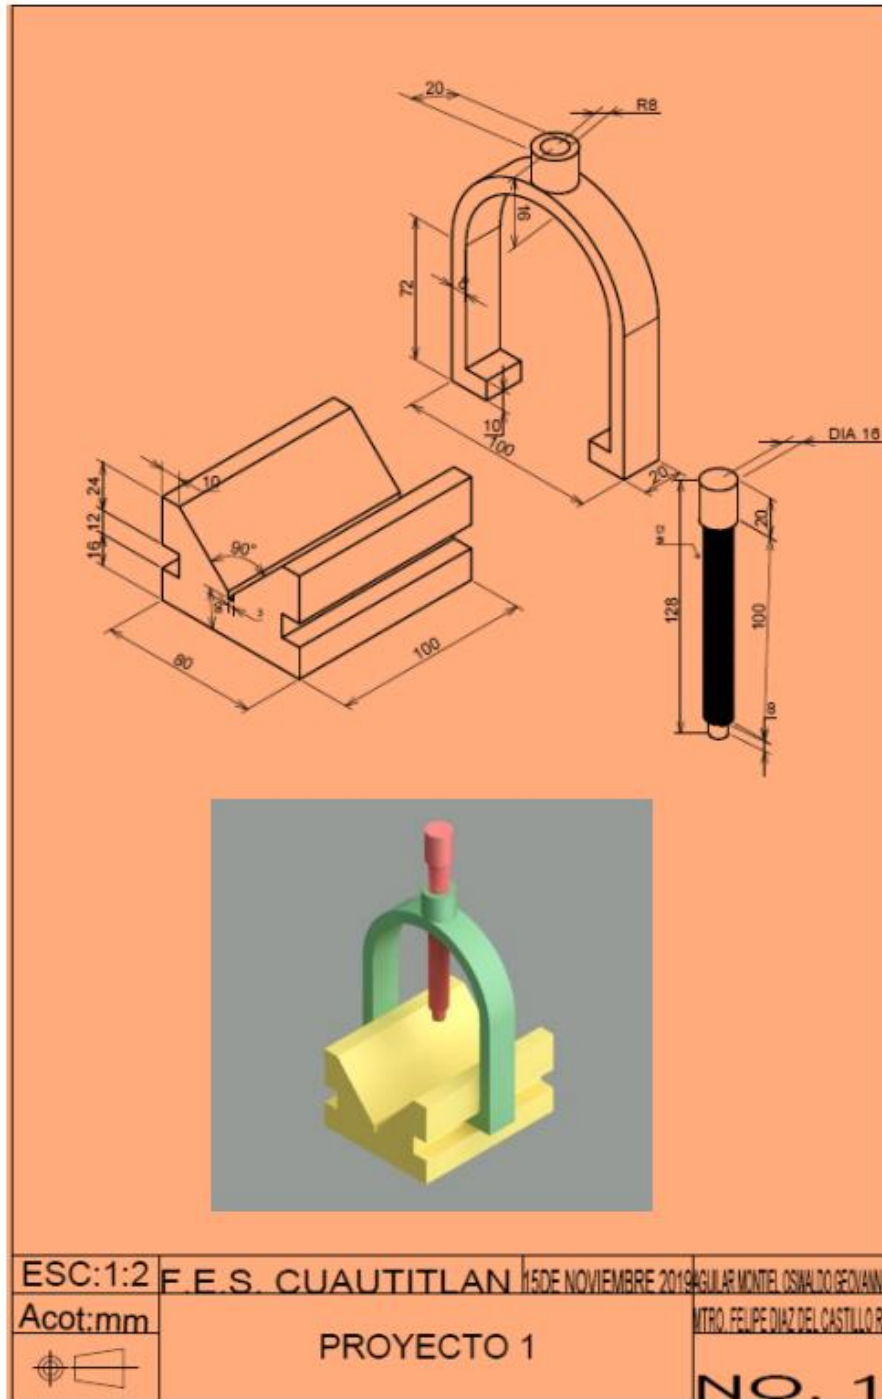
Dibujo de conjunto del ensamble a desarrollar
